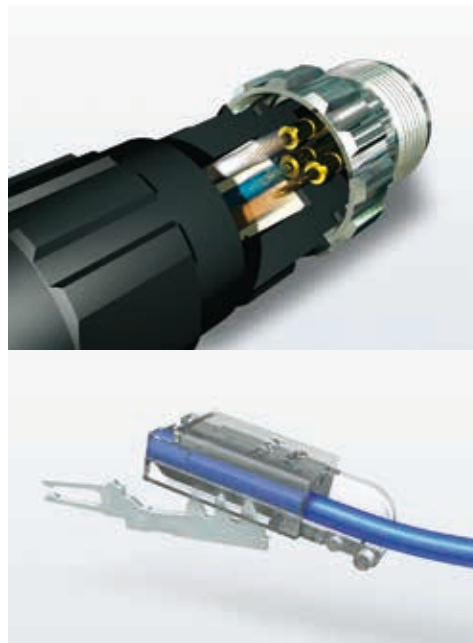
oben: Rundsteckverbinder mit Axial-Piercingkontakten – Quelle: Phoenix Contact
